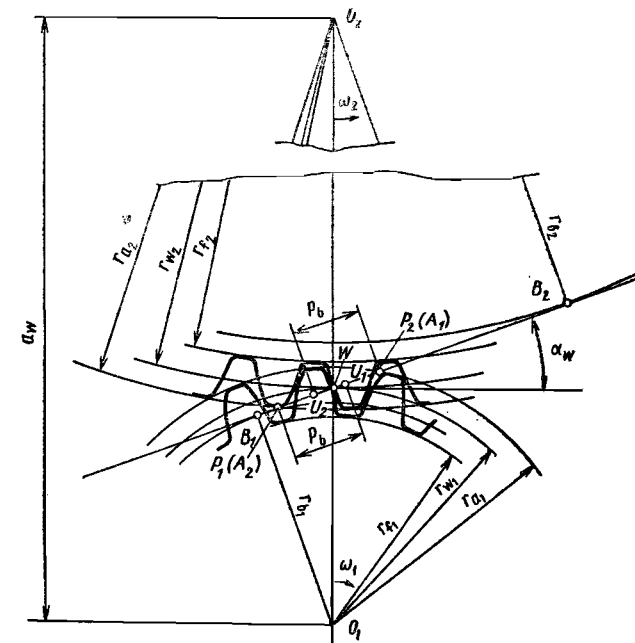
Схема зацепления цилиндрических зубчатых колес без смещения
